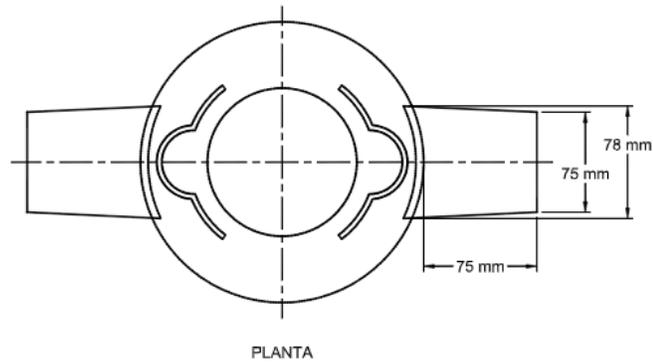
Molde para ensayos de asentamiento, vista Planta
